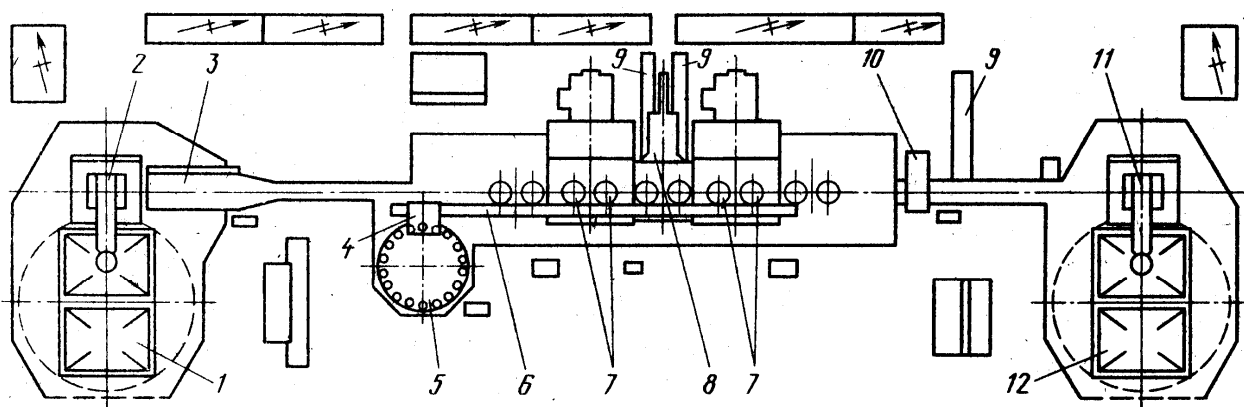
Структура токарного ГРТК з двома універсальними роботами фірми «Комау»: 1 і 12 – ящики із заготовками і обробленими деталями; 2 і 11 – універсальні роботи для завантаження і розвантаження оброблених деталей; 3 – транспортна система; 4 – механізм автоматичної заміни інструменту; 5 – інструментальний магазин; 6 – напрямні механізму автоматичної заміни інструменту; 7 – вертикальні шпindelьні вузли; 8 – система проміжного контролю деталей і кантувач; 9 – механізм видалення бракованих деталей; 10 – система остаточного контролю деталей
